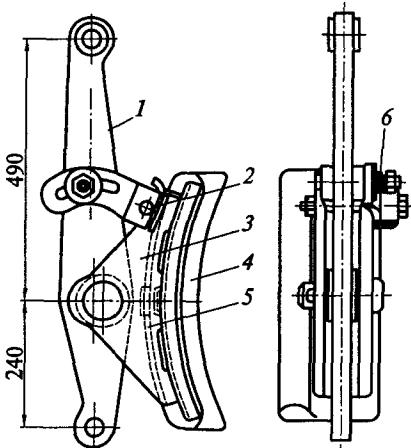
Крепление башмака с тормозной колодкой к подвеске:
